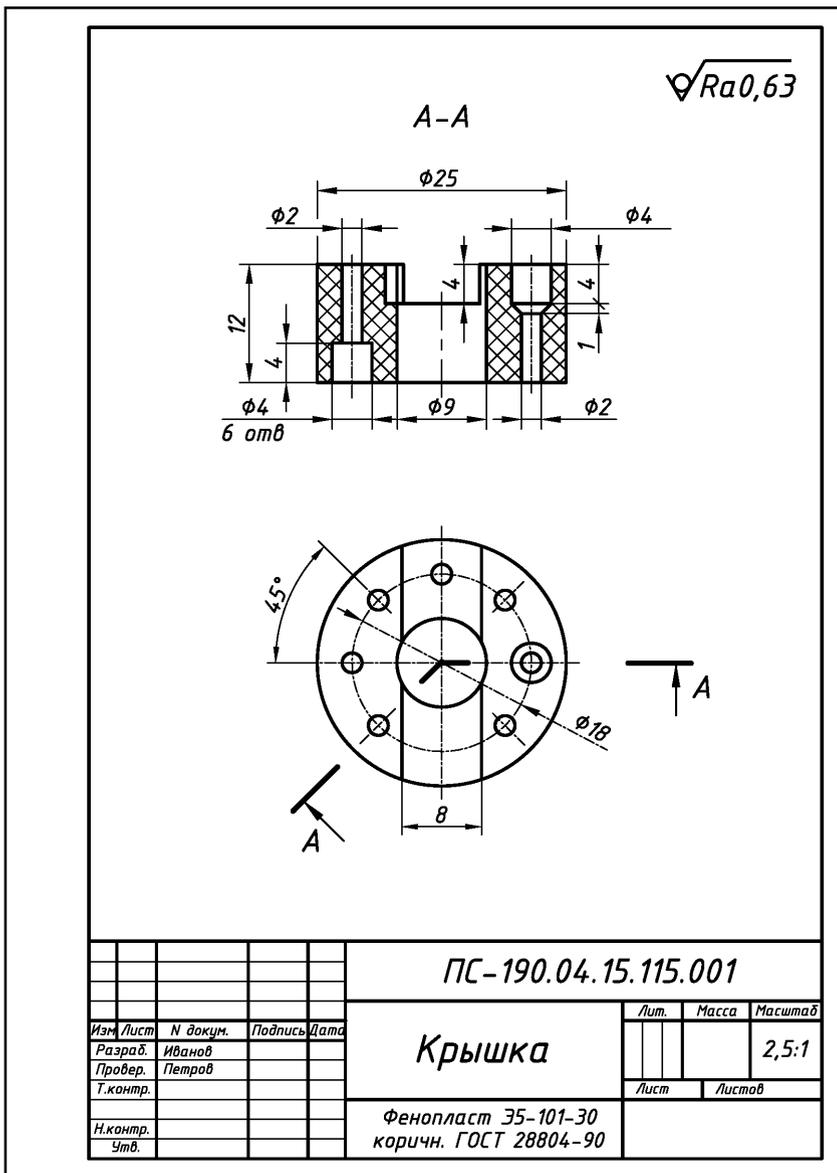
Оформление рабочего чертежа литой детали из пластмассы
